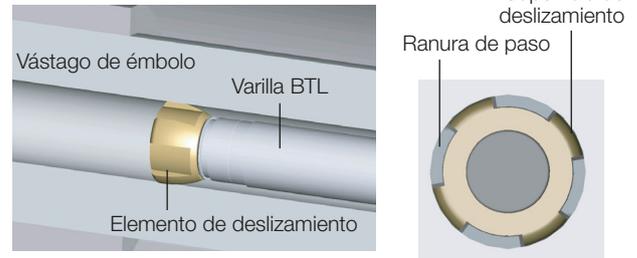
Vista detallada y vista desde arriba del elemento de deslizamiento
